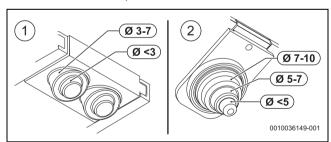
Adaptar las abrazaderas al diámetro del cable
